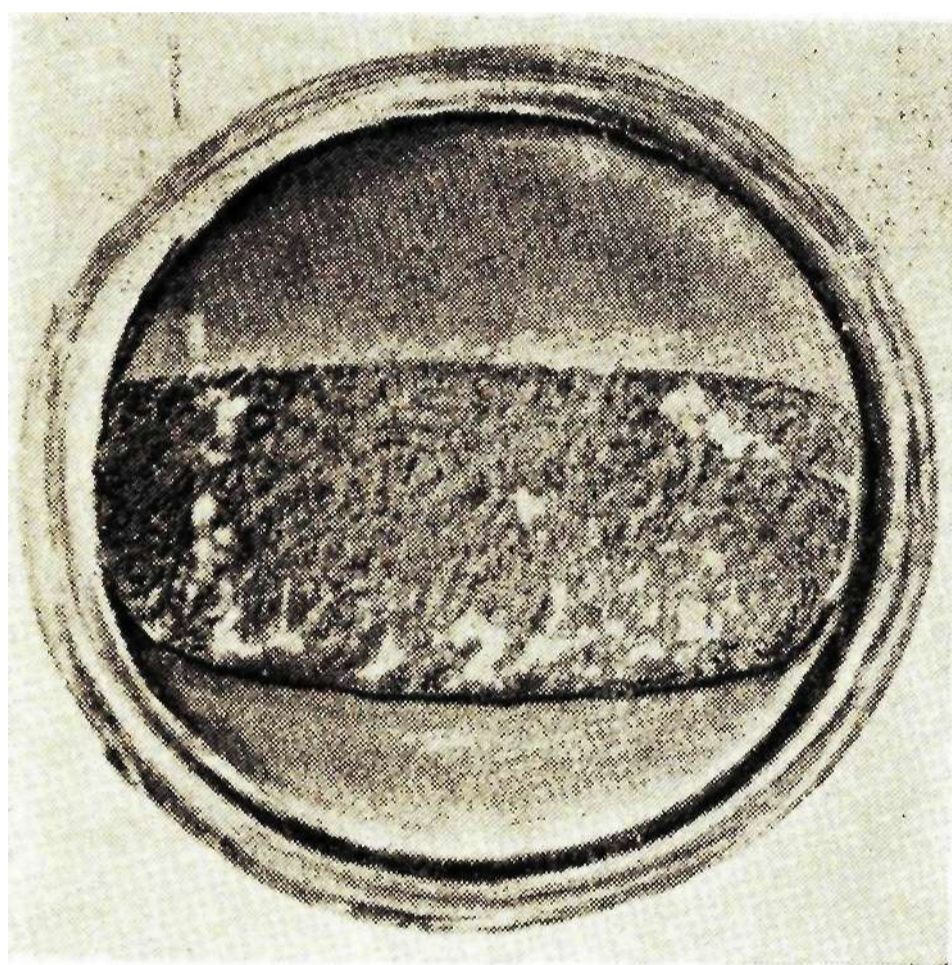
Вид поверхности разрушения при явлении усталости металла
